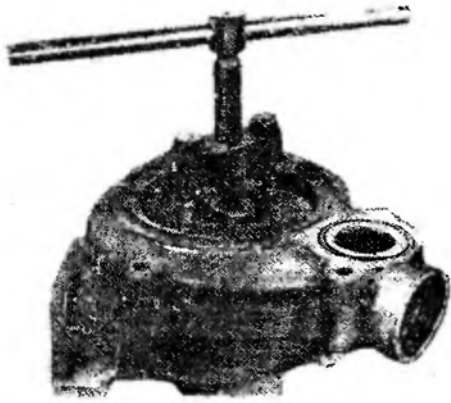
Снятие крыльчатки съемником подшипников карданных валов
